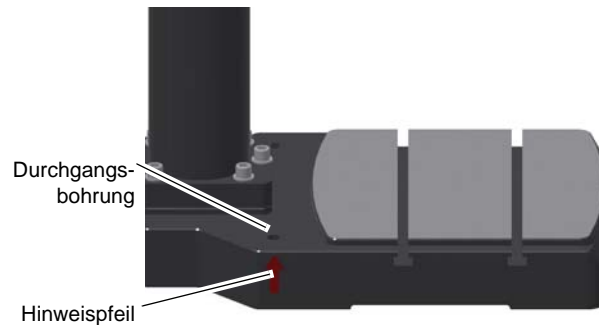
Kennzeichnung der Befestigungspunkte B34H
